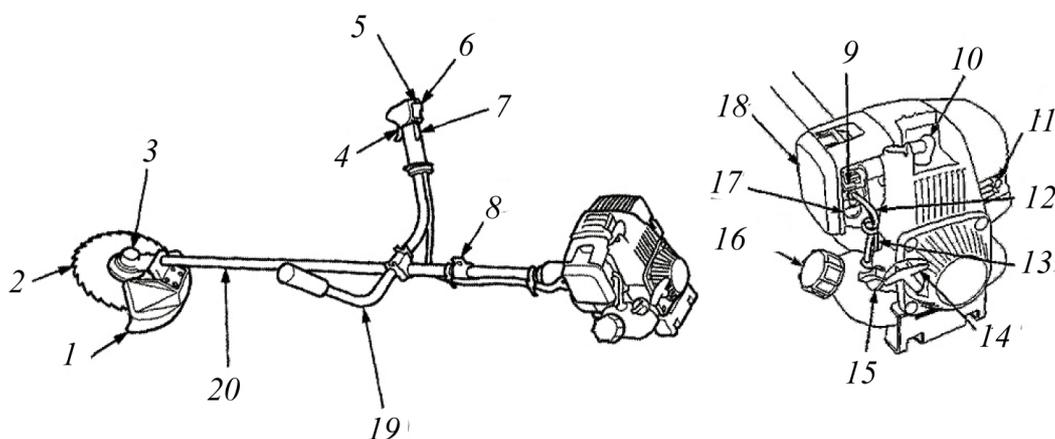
Мотокусторез «Stihl»: 1 – защитный щиток; 2 – пильный диск; 3 – угловая зубчатая передача; 4 – рычаг газа; 5 – выключатель зажигания; 6 – блокировка ручки газа (круиз-контроль); 7 – кнопка контроля оператора; 8 – крепление ремня; 9 – рычаг подсоса; 10 – крышка свечи зажигания; 11 – искроуловитель; 12 – трубка возврата топлива; 13 – трубка подачи топлива; 14 – стартер; 15 – масляный фильтр; 16 – топливный бак; 17 – топливный насос; 18 – крышка воздушного фильтра; 19 – U-образная рукоятка; 20 – штанга
